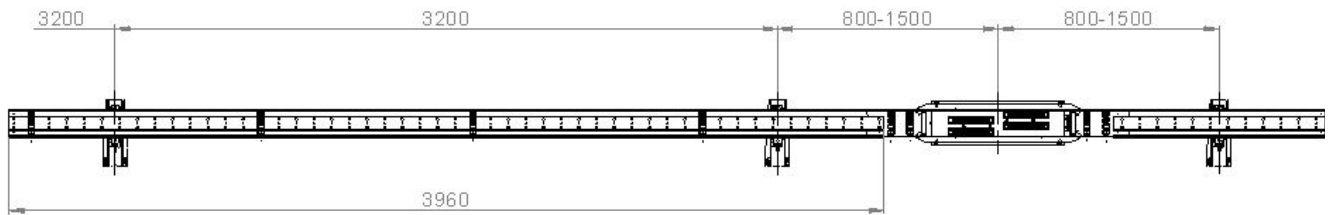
Abstandsmaße ProShell 128 mit Schleifleitungssystem 0812
